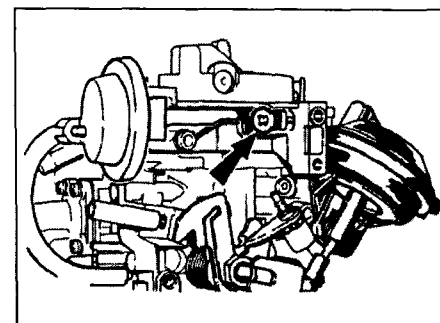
,б. Фиксатор (указан стрелкой) крепления рычага диафрагмы
